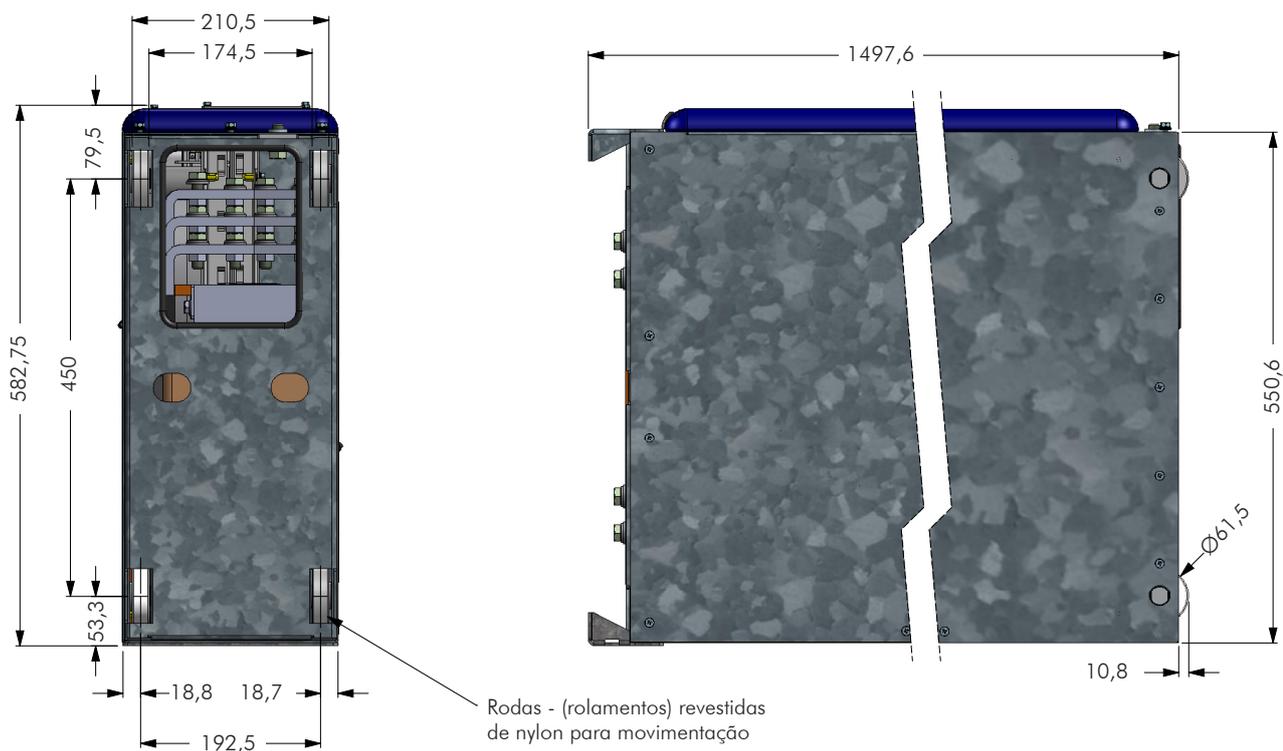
UR11: vista inferior e vista lateral em corte (mm)
